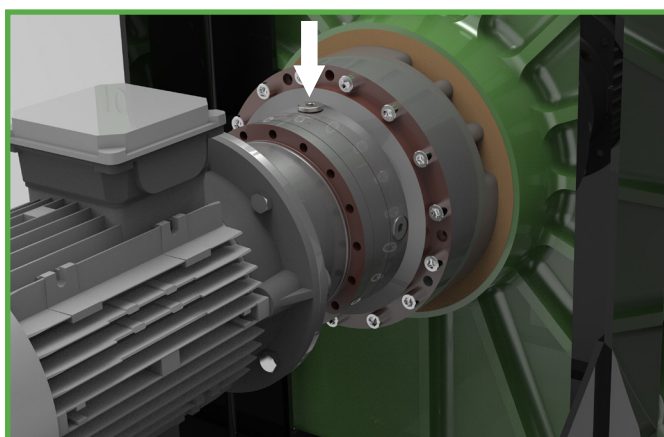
Befestigen des Befüllstopfens für das Getriebe
